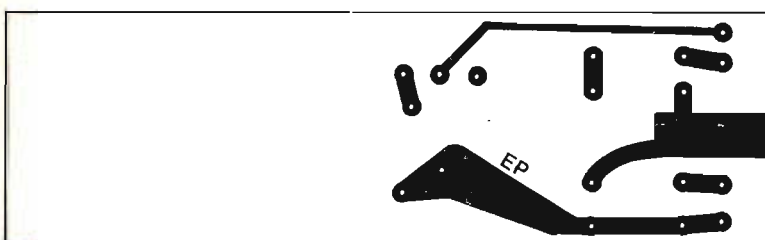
Disegno del circuito stampato in grandezza naturale che il lettore dovrà riprodurre prima di iniziare le operazioni di assemblaggio dei componenti del circuito del minitester.
